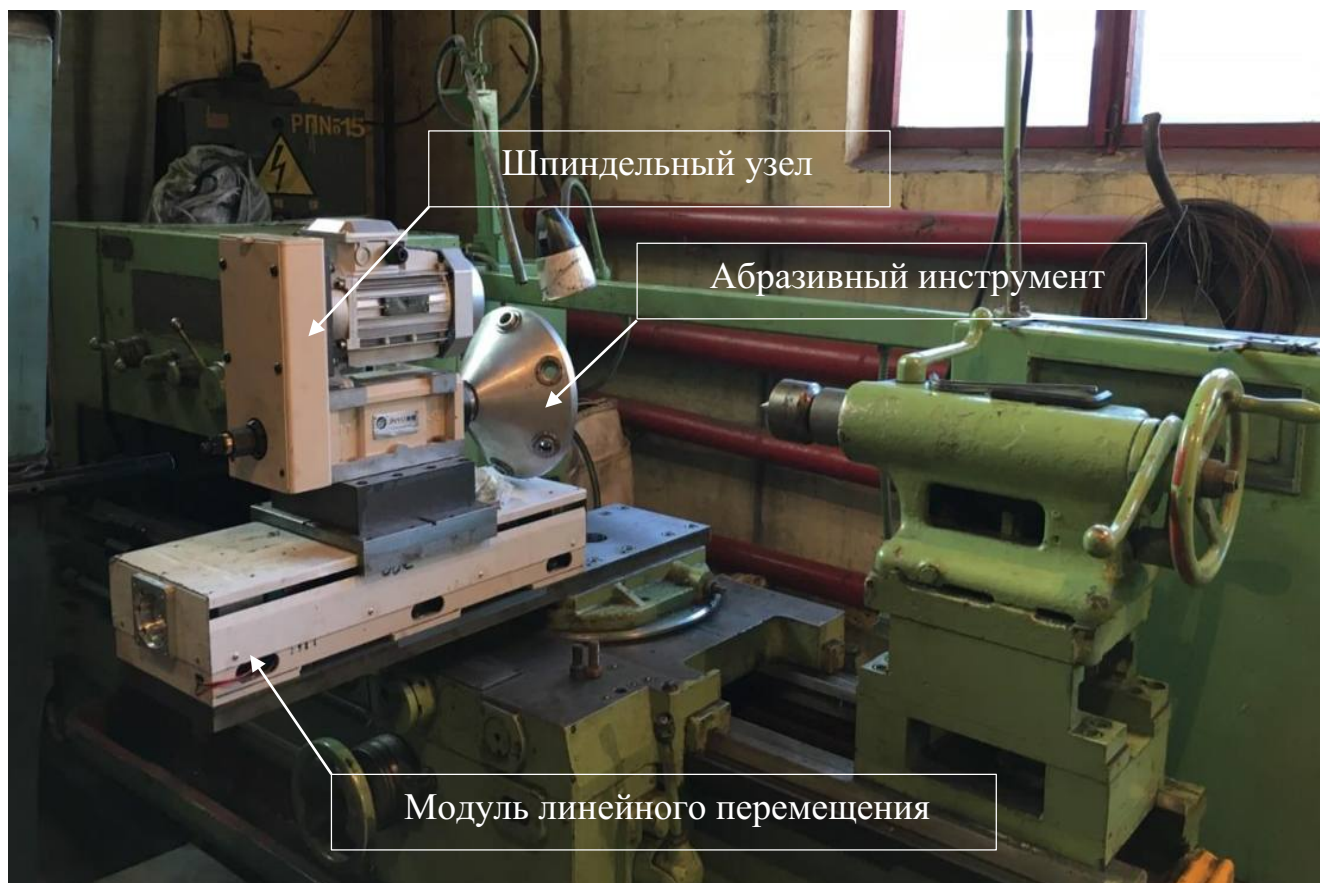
Сферотокарный станок МК6033, общий вид
